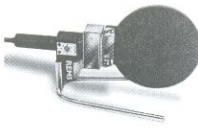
Аппарат «РЕМС ССГ» для сварки труб встык
